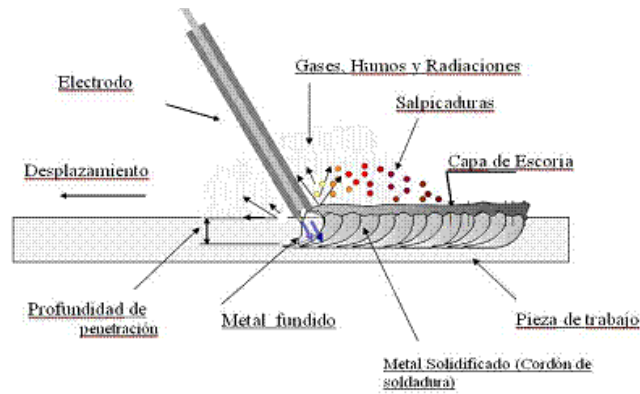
Soldadura con electrodo revestido.
